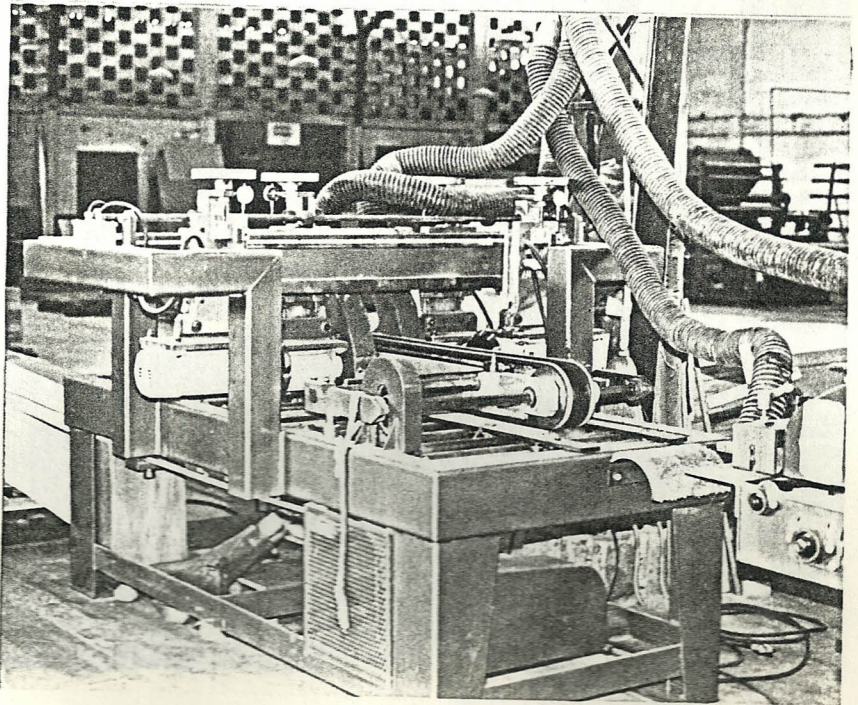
Corte Lineal con máquina V-Grooving.
